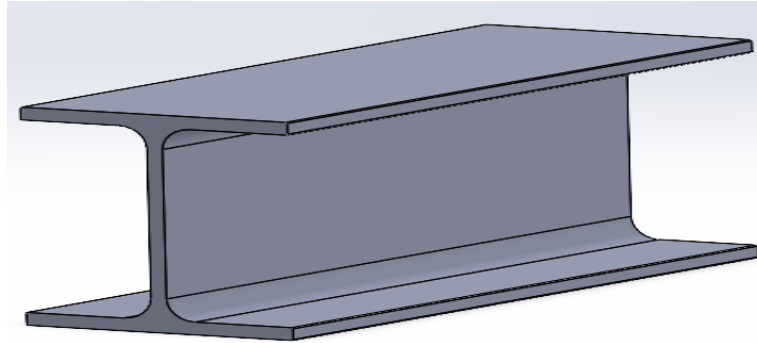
Géométrie modélisée d'une extrusion I 3D 6005A-T6
